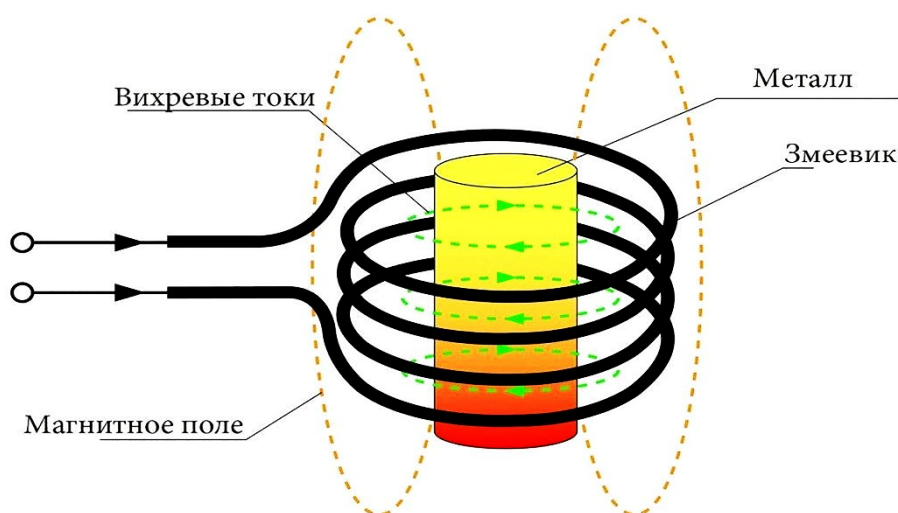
Прямой нагрев материала (металлической заготовки, помещенной внутрь индуктора) в ИНУ
